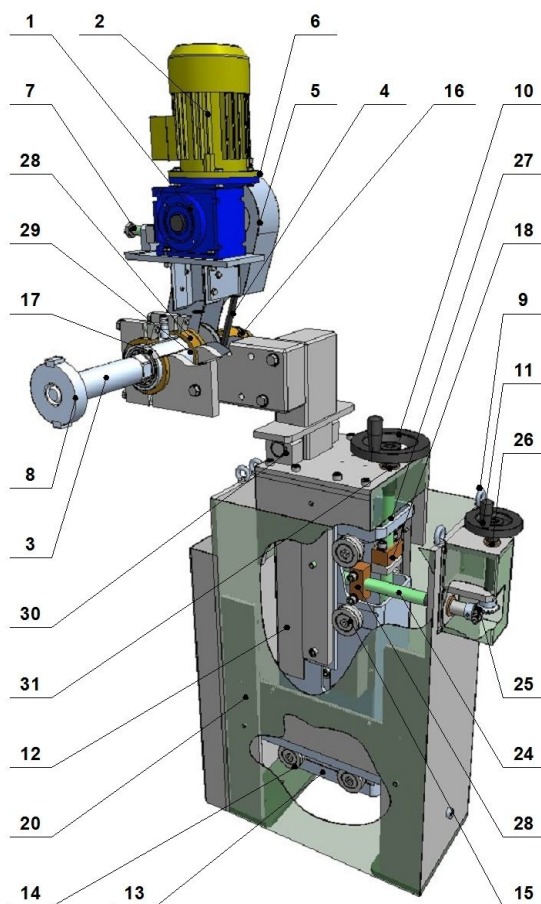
3D model držáku pyrometrů [převzato z 28]
